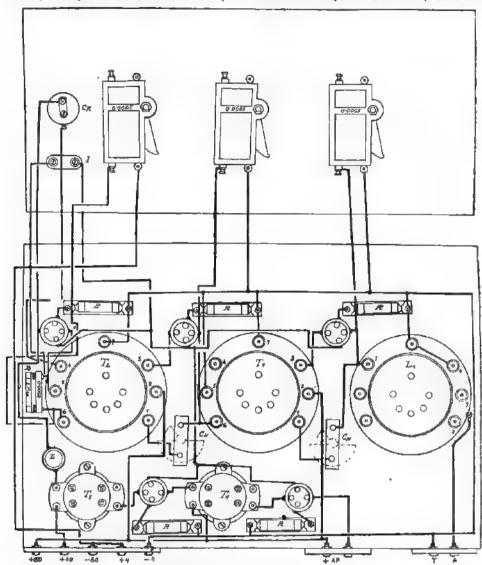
, - Sohema costruttivo osservare attentamente la disposizione dei collegamenti.
